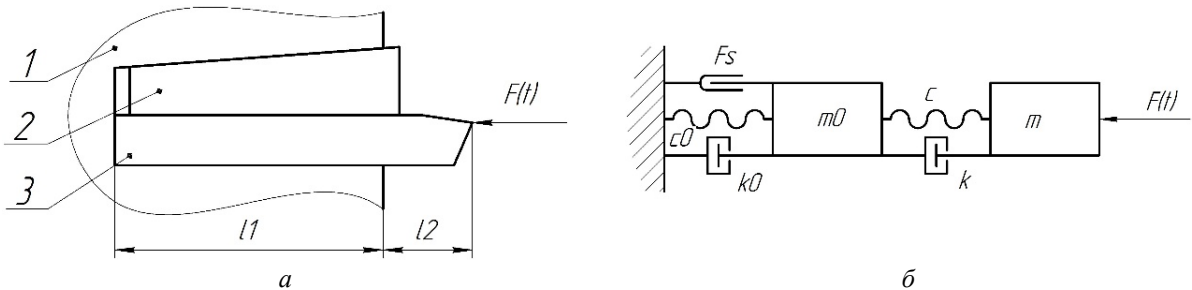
Конструктивна (а) та розрахункова (б) схеми пресового з'єднання
